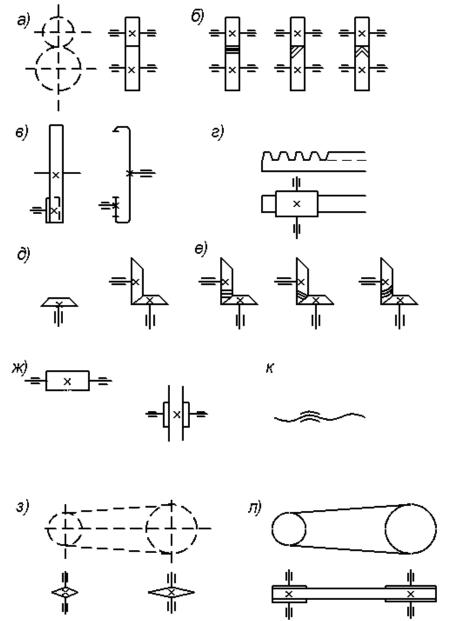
Условные обозначения передач на кинематических схемах: a – цилиндрическая зубчатая передача;  $\delta$  – цилиндрические передачи соответственно с прямыми, косыми и тангенциальными зубьями;  $\epsilon$  – цилиндрическая зубчатая передача с внутренним зацеплением;  $\epsilon$  – зубчато-реечная передача;  $\delta$  – коническая зубчатая передача;  $\epsilon$  – конические передачи соответственно с прямыми тангенциальными и круговыми зубьями; ж – червячная передача;  $\epsilon$  – цепная передача;  $\epsilon$  – передача винт–гайка;  $\epsilon$  – ременная передача
